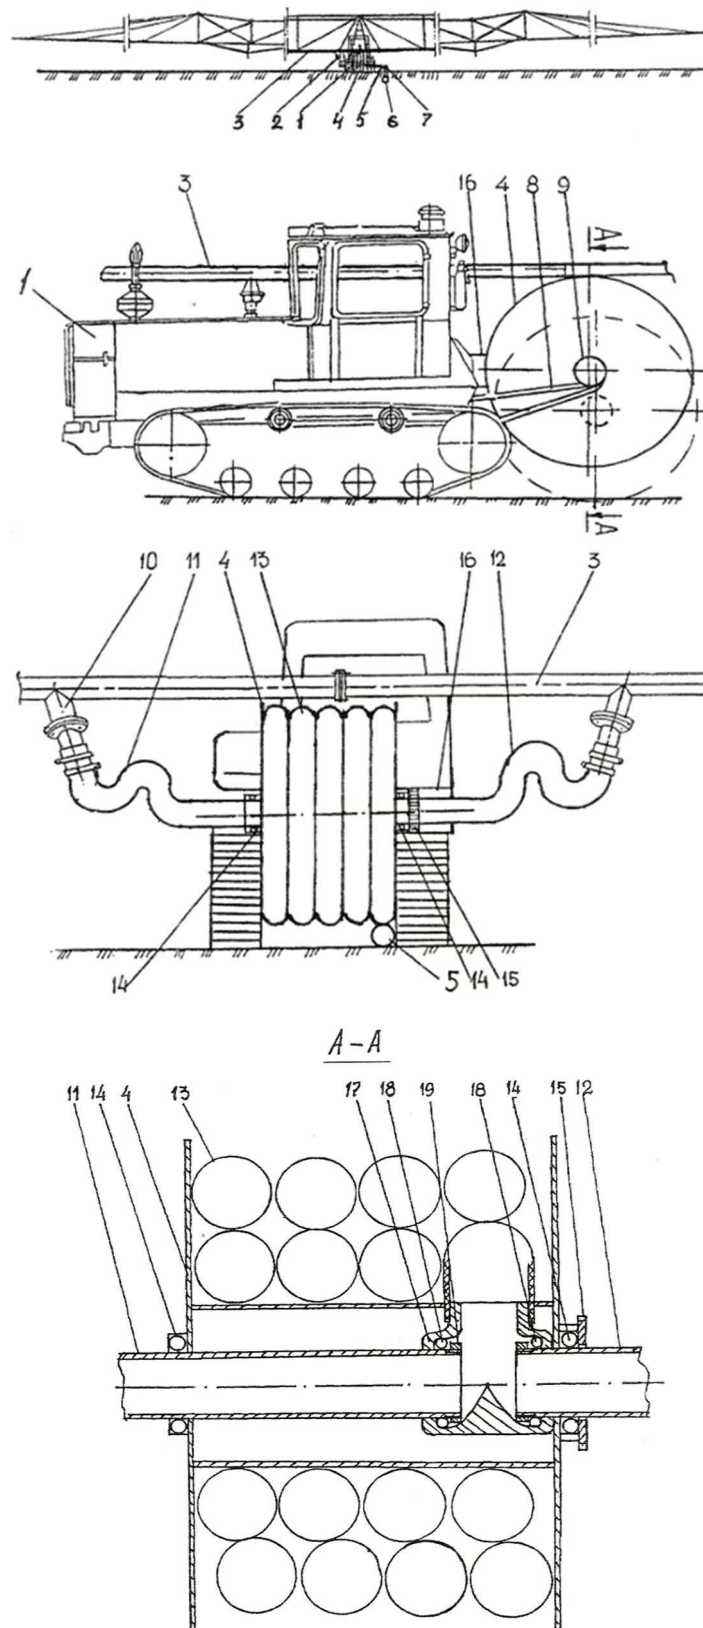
Консольный дождевальный агрегат (патент RU 2409936)
